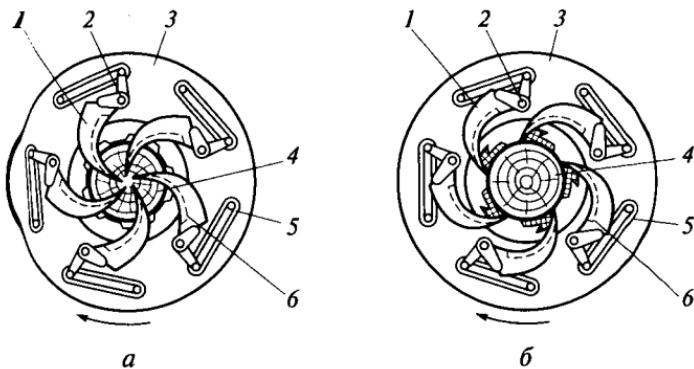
Схемы короснимающего механизма роторного окорочного станка с прижимом короснимателей резиновыми кольцами:
